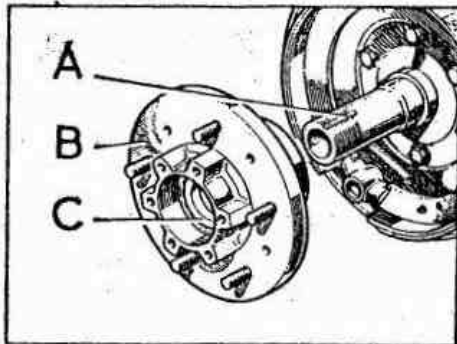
Desmontaje del conjunto de la mangueta y cojinete
